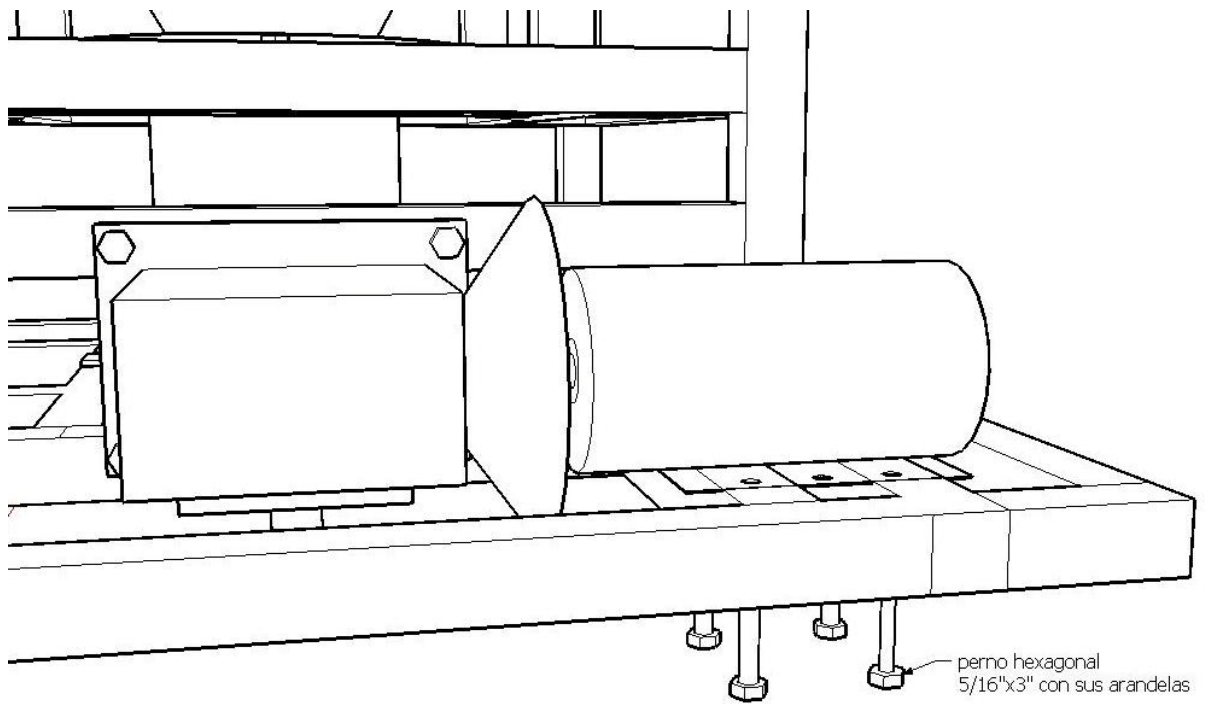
El alineamiento del motor con la caja reductora debe ser preciso.
